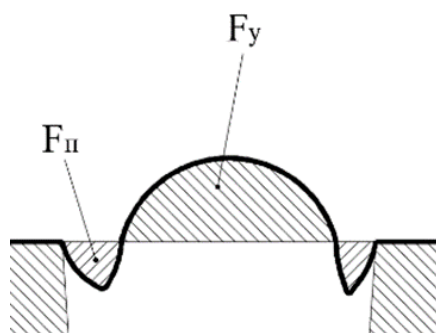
Схема формирования усиления и подрезов сварного шва
